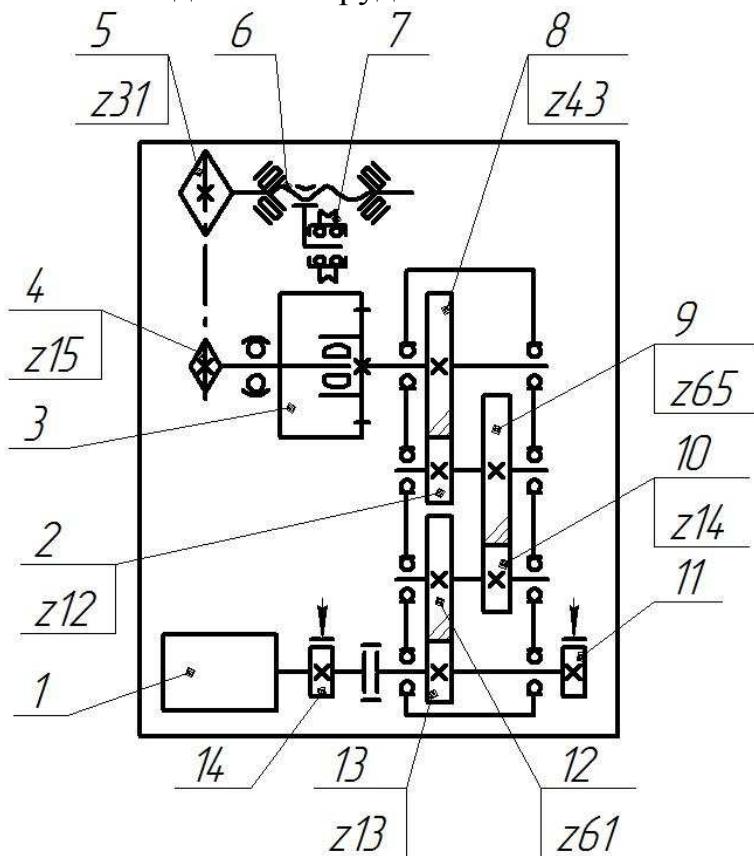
Кинематическая схема стреловой лебедки: 1 – электродвигатель, 2, 8-10, 12, 13 – шестерни, 3 – барабан, 4, 5 – звездочки, 6 – однозаходный червяк, 7 – канатоукладчик, 11, 14 – тормоза
